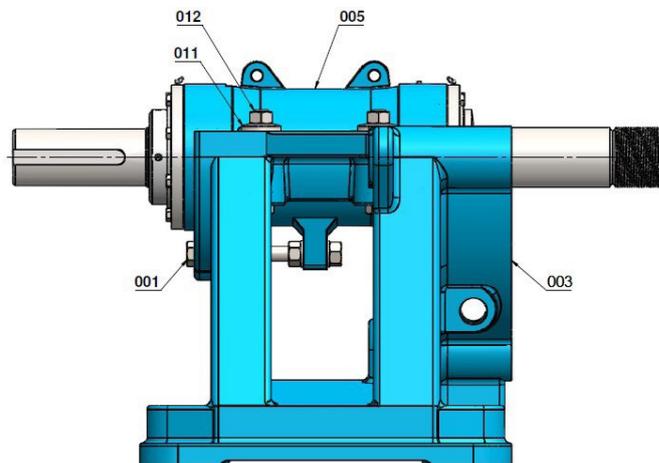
MONTAGEM DO CONJUNTO MECÂNICO
